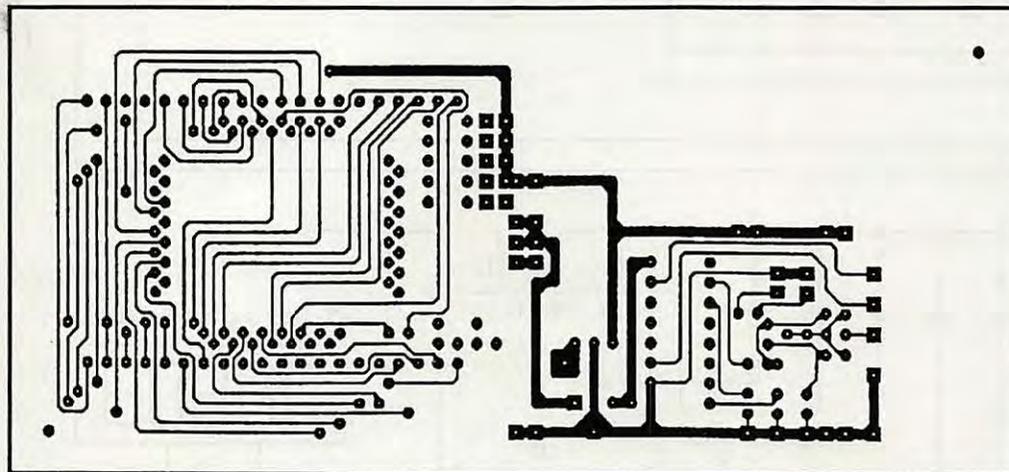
Circuit imprimé double face, trous métallisés, côté soudures.
